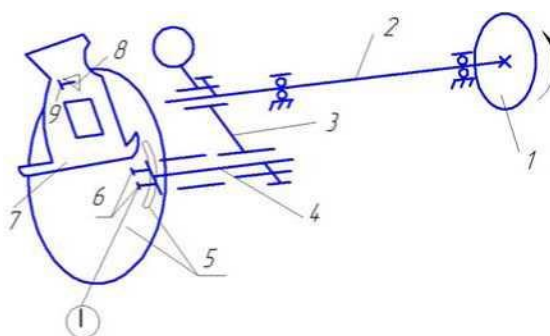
Механизм нитепритягивателя. 1 - шкив - маховик; 2 - главный вал; 3 - кривошип с противовесом; 4 - палец; 5 - диск с пазом; 6 - винты; 7 - закаленная отполированная скоба нитепритягивателя; 8 - отверстие в скобе; 9 - винт.
